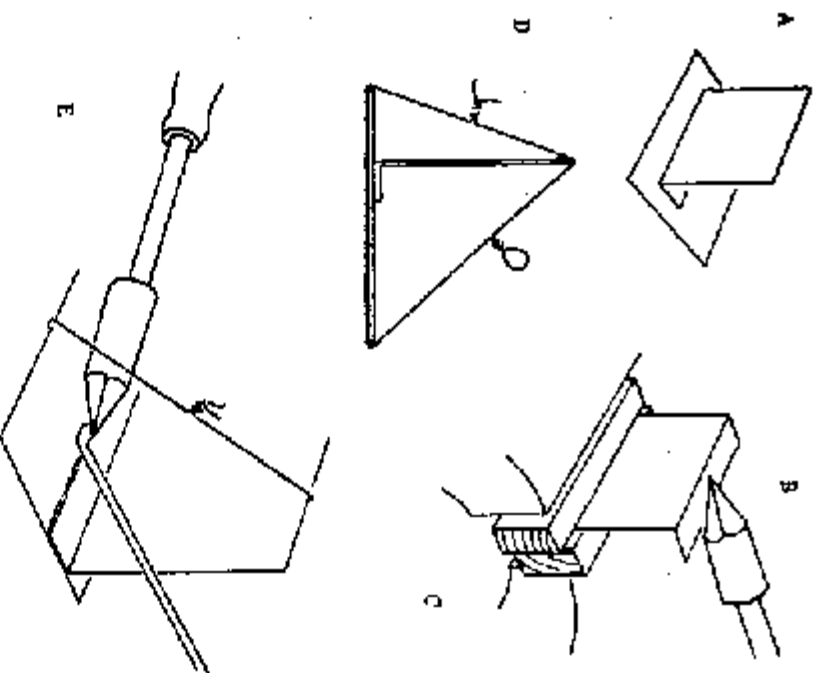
Las partes que deben unirse se ensazan con soldadura y se unen con alambres: (A) rebordado; (B) aplíquese fundente y mójese lentamente el caudín; (C) úsense mordazas de madera en las quijadas; (D) refuerzase el alambre de hierro; (E) pásese el caudín a lo largo de la unión.
